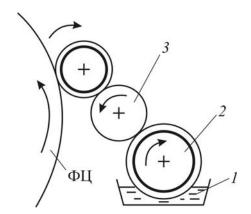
Увлажняющий аппарат контактного типа с непрерывным питанием: I — корыто; 2 — валик с оболочкой; 3 — раскатной цилиндр; Φ Ц — формный цилиндр
